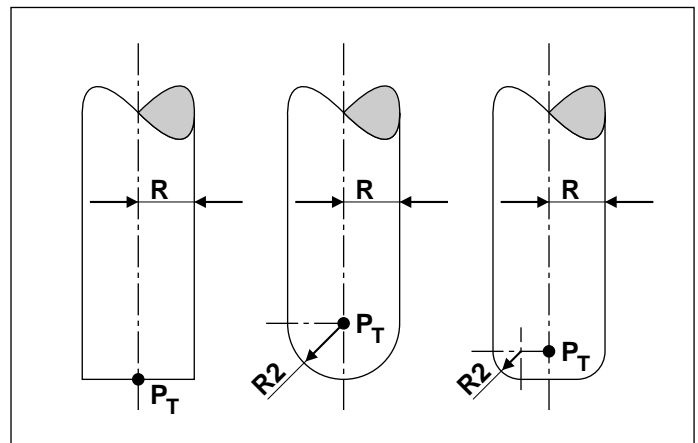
Werkzeug-Radien R, R2 und -Bezugspunkt P, beim Schaft-, Radius- und Eckenradiusfräser
